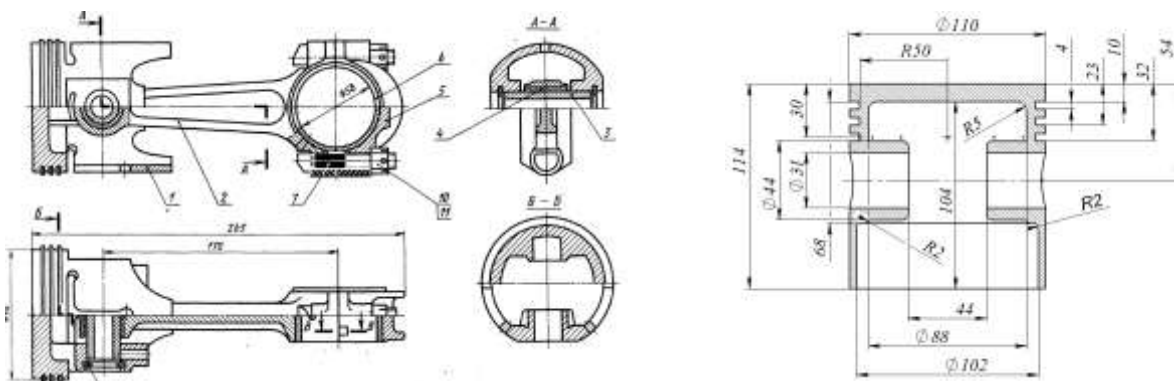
Чертежи сборочной единицы «поршень в сборе» и наиболее значимой детали «поршень». 1-поршень, 2-поршневой палец, 3-шатун, 4- крышка шатуна,5,6-шпилька и гайка
